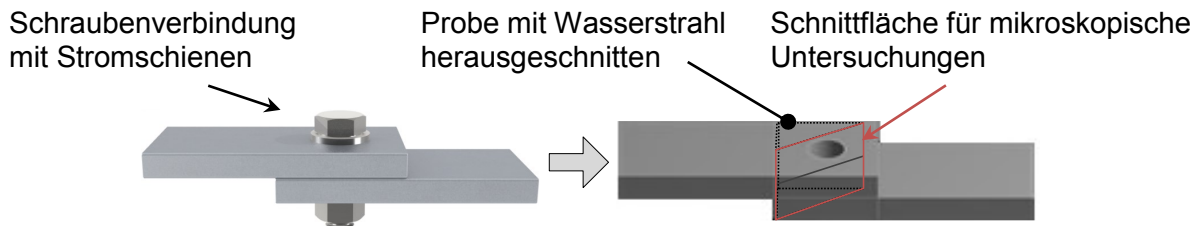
Mit einem Wasserstrahl geschnittene Probe aus einer thermisch belasteten Schraubenverbindung mit Stromschienen und gerillten Kontaktflächen
